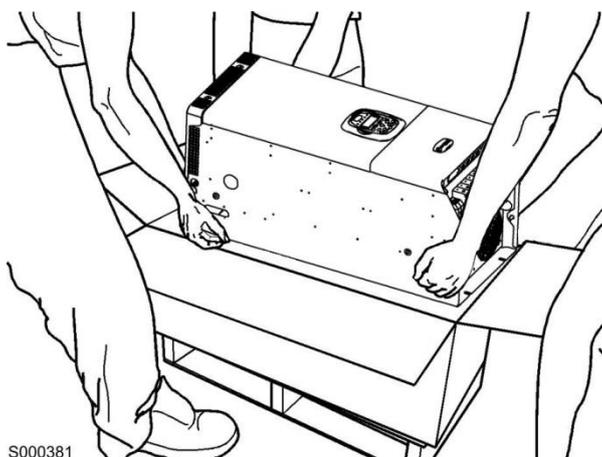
Estrazione dell'AC/DC UNIT dall'imballaggio
